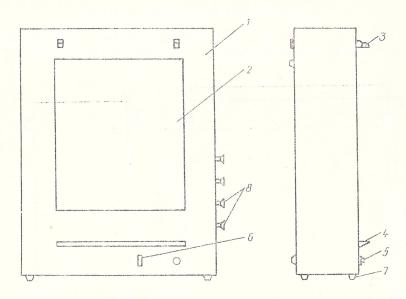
Негатоскоп общего назначения с диафрагмирующими шторками НІЦ-48. Общий вид
